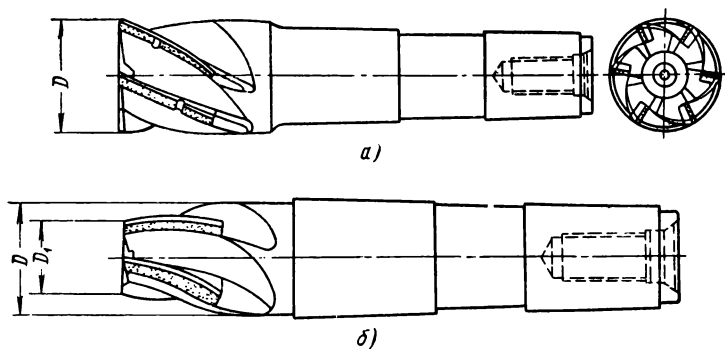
Концевые фрезы с напаянными винтовыми зубьями из нескольких твердосплавных пластинок
